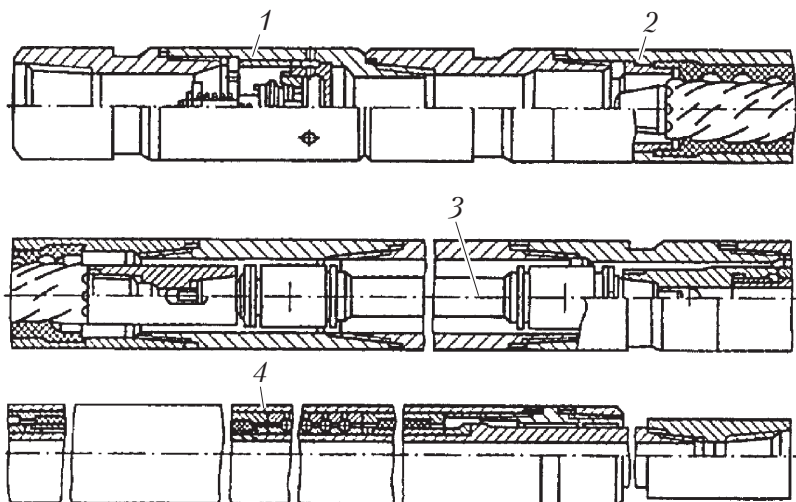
Винтовой (объемный) забойный двигатель Д1-195
